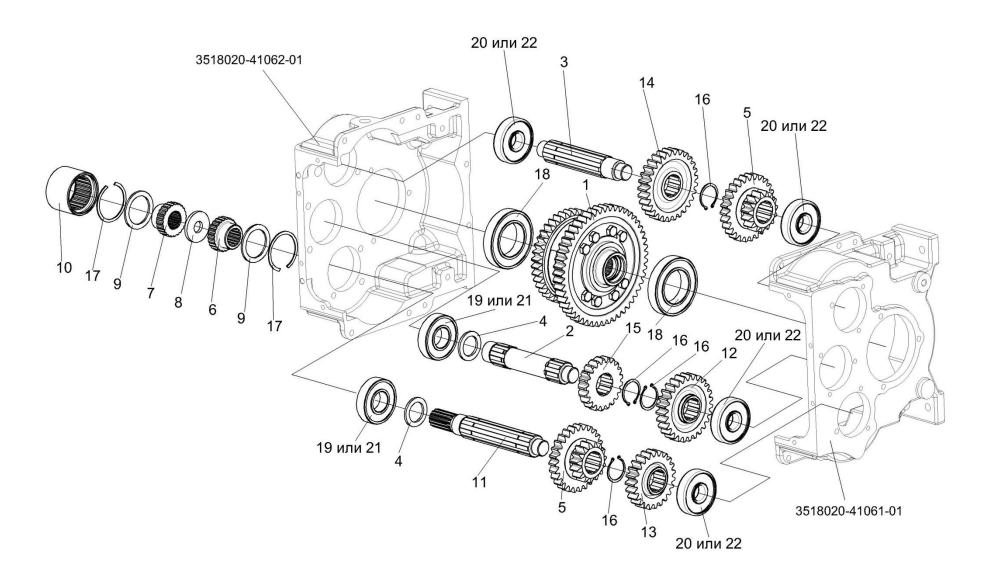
Коробка диапазонов 3518020-46150 (валы, шестерни)
